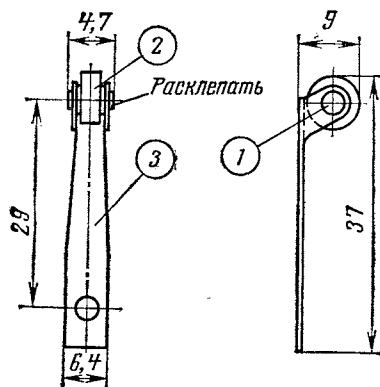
Фиксатор: 1 — ось; 2 — валик; 3 — пружина.
